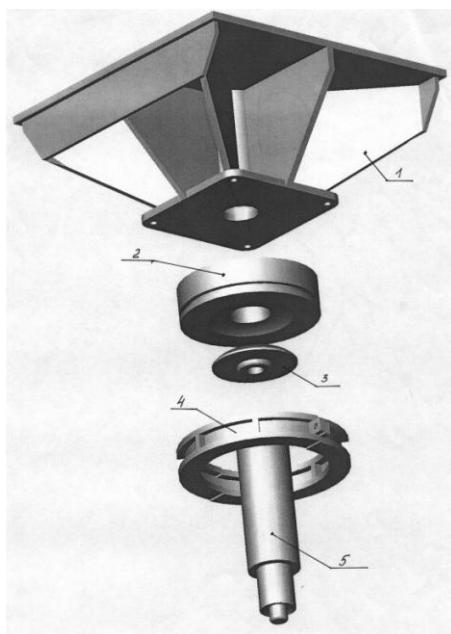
Конструкция узла соединения опоры портала с тележкой (1 – башмак; 2 – стакан; 3 – полусфера; 4 – полуобоймы; 5 – шкворень).
